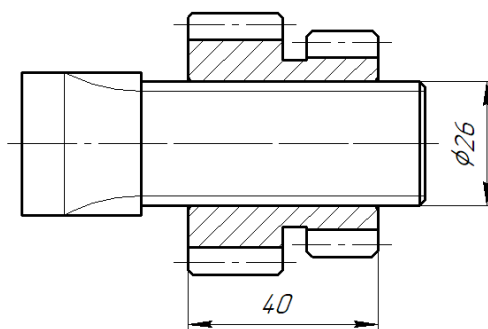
Соединение блока шестерен с валом токарного станка
